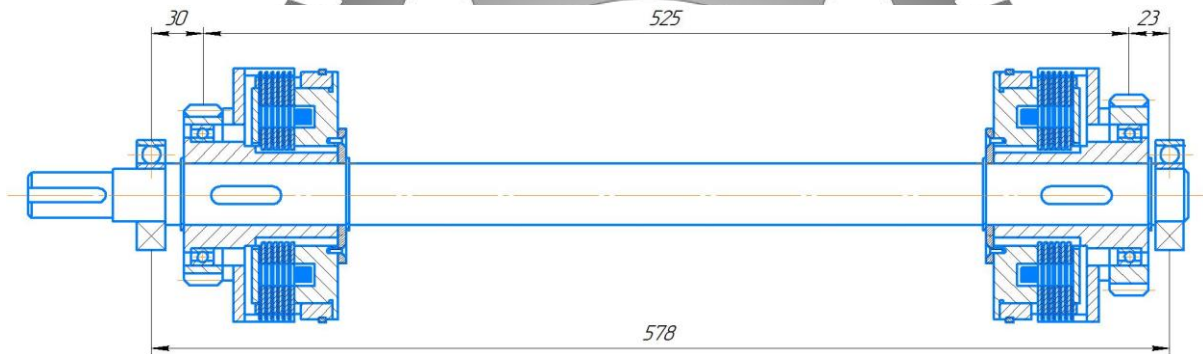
Положення зубчастих коліс та небезпечний переріз вала І.
